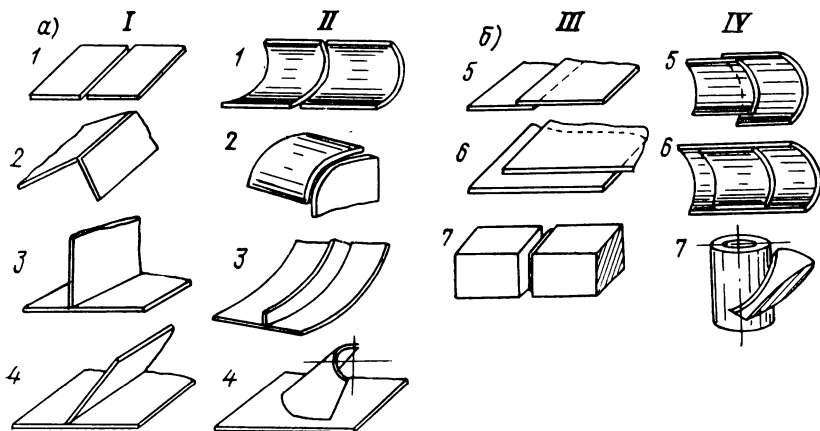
Сборочные сопряжения, собираемые под сварку: а — линейные; б — поверхностные.
